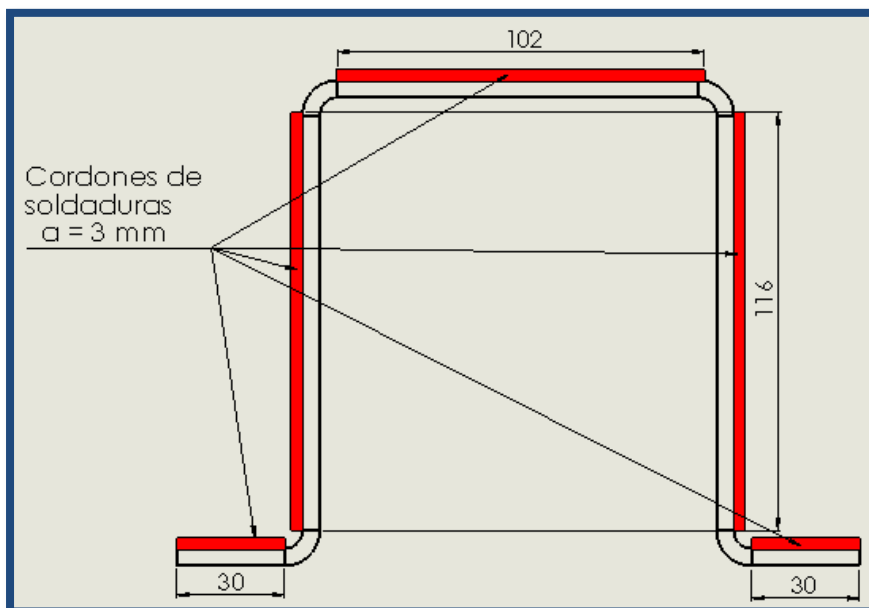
Vista de los cordones de soldadura realizados en el parante.
